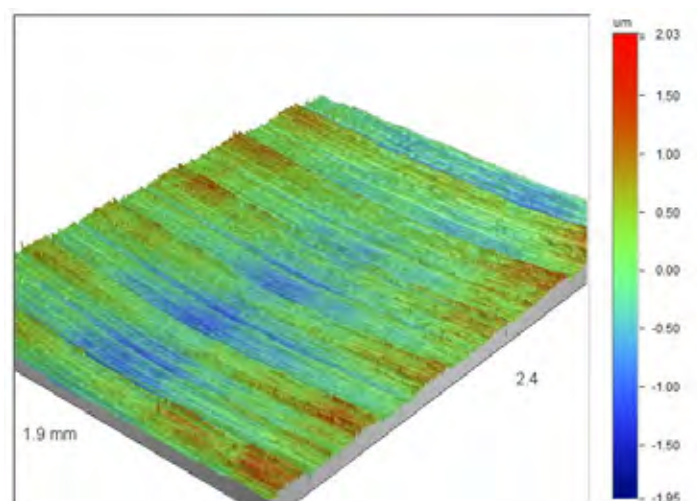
Representação tridimensional da superfície do material GUF, usinado sob condição C4.
